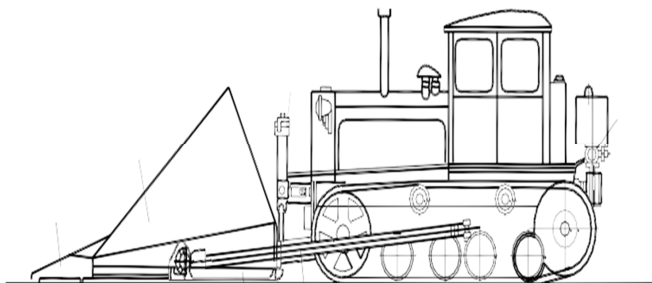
Кусторез – КБ 2.8 для подготовительных работ: 1 – колун; 2 – отвал; 3 – гидроцилиндр; 4 – гидропривод; 5 – ло-вители; 6 – толкающая рама; 7 – ложка; 8 – нижняя рама
